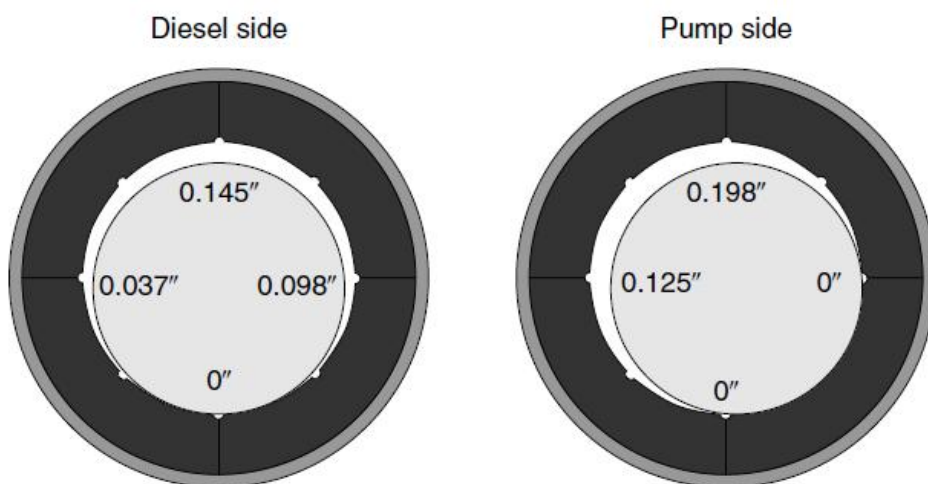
bearing nước dạng cutlass với khe hở vượt quá giới hạn.
